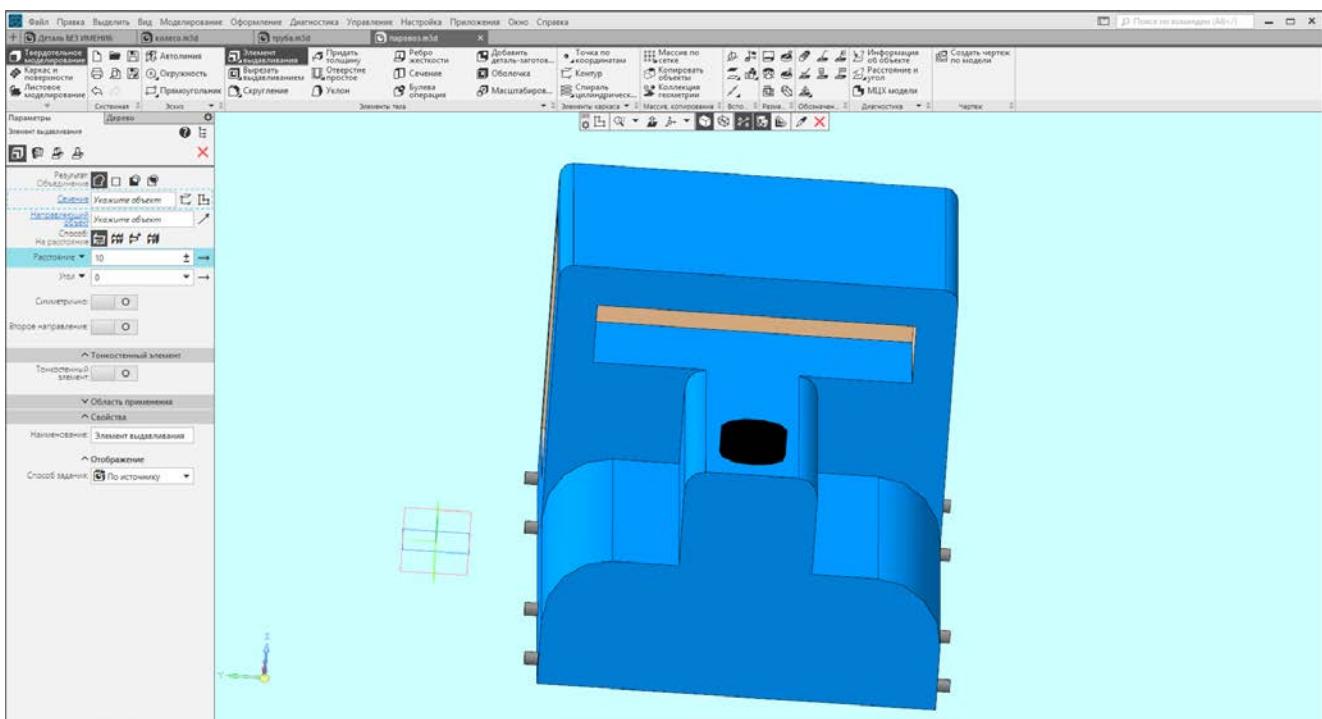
Готовая трехмерная модель корпуса паровоза
